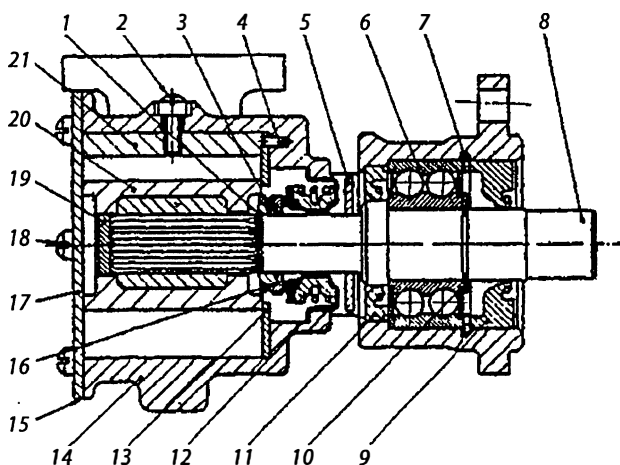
Водяной насос охлаждения компрессора: 1 — стопорное кольцо; 2 — винт; 3 — посадочное кольцо; 4 — штифт; 5 — отбойный диск; 6 — шарикоподшипник; 7 — стопорное кольцо; 8 — вал; 9 — уплотнение; 10 — стопорное кольцо; 11 — уплотнение; 12 — графитовое уплотняющее кольцо; 13 — стопорное кольцо; 14 — корпус; 15 — прокладка; 16 — стальное уплотняющее кольцо; 17 — крышка; 18 — винт; 19 — уплотнение; 20 — рабочая крылатка; 21 — кулачок
